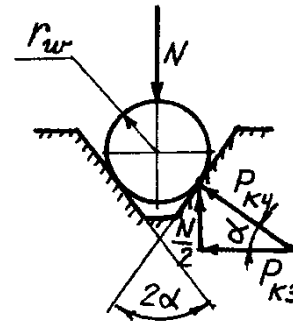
Розрахункова схема шарикової напрямної / Fig. 3. The design scheme of the ball guide
